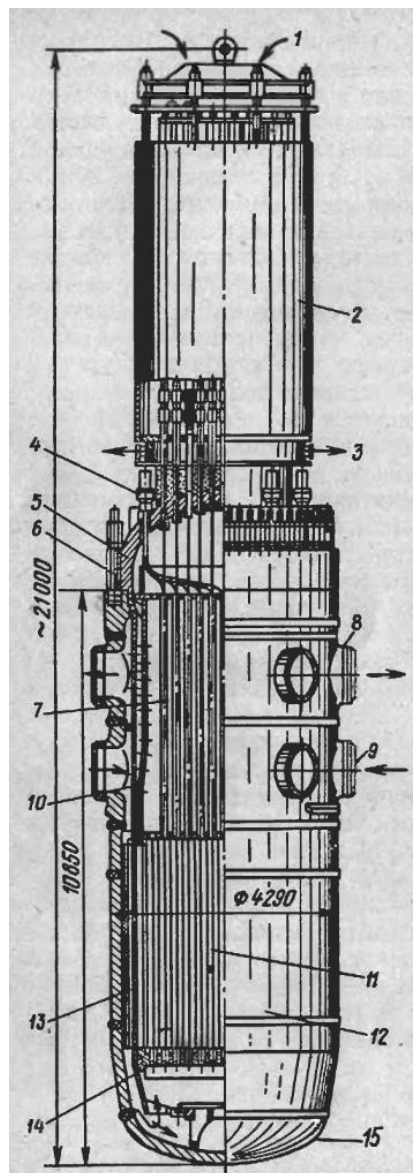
Общий вид реактора ВВЭР-1000 [3, с.42]:
